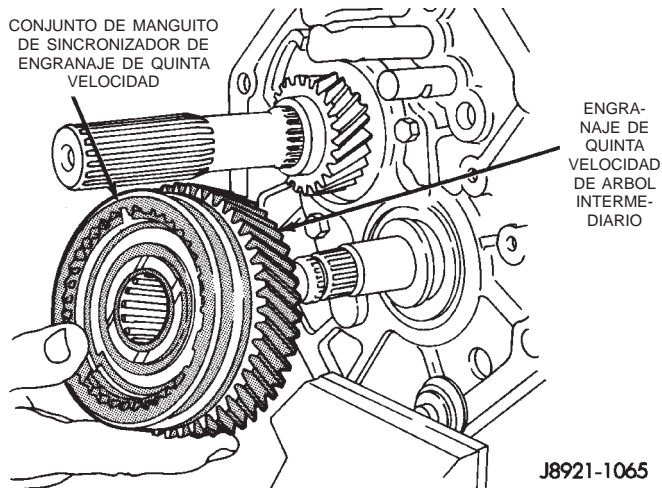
Desmontaje de conjunto de sincronizador y engranaje de quinta velocidad
